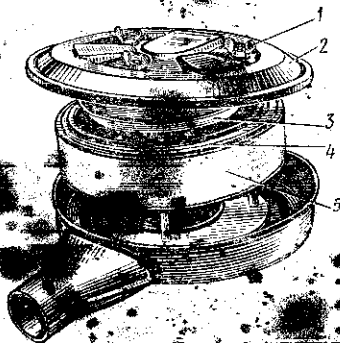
Воздушный фильтр карбюратора 210F-11070: 1 — барашковая гайка; 2 — крышка корпуса; 3 — демпфирующая вставка; 4 — фильтрующий элемент; 5 — лента (фильтр предварительной очистки)
